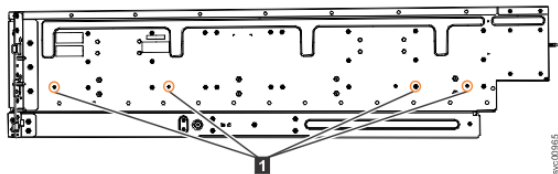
Расположение винтов для прикрепления внутренней направляющей к корпусу
